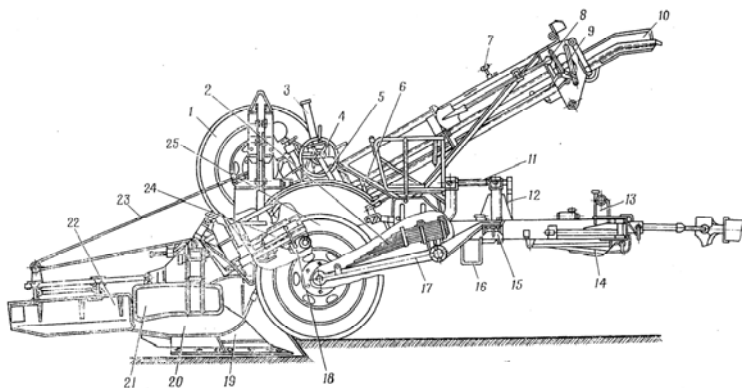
Минный заградитель ПМЗ-4 в рабочем положении (вид справа): 1 – запасное колесо; 2 – рессора; 3 – кожух винта механизма подъема; 4 – штурвал механизма подъема обратных отвалов; 5 – рукоятка механизма подъема плуга; 6 – рукоятка управления фрикционом; 7 – зажим крепления приемного лотка в транспортном положении; 8 и 9 – рукоятки управления фрикционом из кузова тягача; 10 – приемный лоток; 11 – винт механизма блокировки рессор; 12 – рукоятка механизма блокировки рессор; 13 – упор с зажимами для крепления направляющего лотка в транспортном положении; 14 – опорная стойка (в транспортном положении); 15 – поворотный кронштейн механизма блокировки рессор; 16 – подножка; 17 – балансир; 18 – рукоятка переключения коробки шага минирования; 19 – основание плуга; 20 – корпус плуга; 21 – прижим; 22 – обратный отвал; 23 – трос лебедки механизма подъема; 24 – мина под механизмом перевода взрывателей; 25 – колесо
